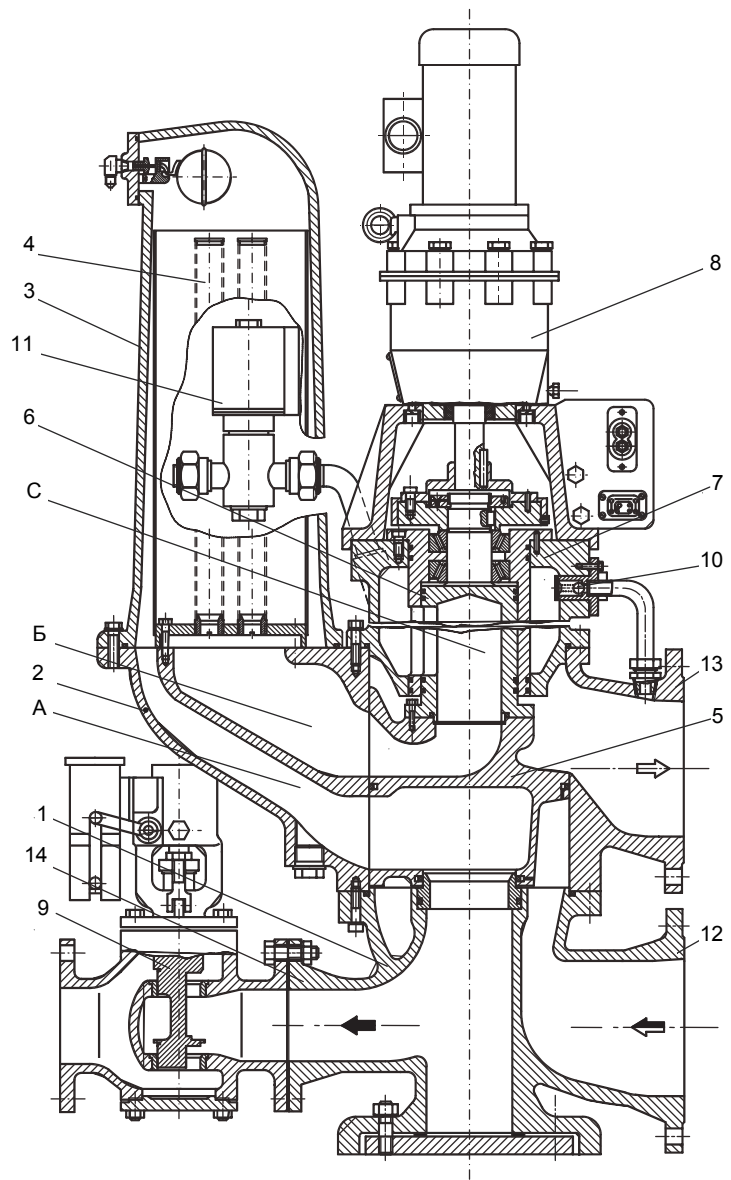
Саморегенерирующийся фильтр СРФД-120: 1-основание; 2-корпус фильтра; 3-фильтровальная камера; 4-ФЭ; 5-распределитель потоков; 6-распределительный золотник; 7-камера продувочного воздуха; 8-электропривод; 9-быстрозапорный управляемый клапан; 10-невозвратный клапан; 11-клапан продувочного воздуха; 12-впускной патрубок; 13-выпускной патрубок; 14-патрубок сброса грязи; А-входная полость корпуса; Б-выходная полость корпуса; С-продувочные окна
